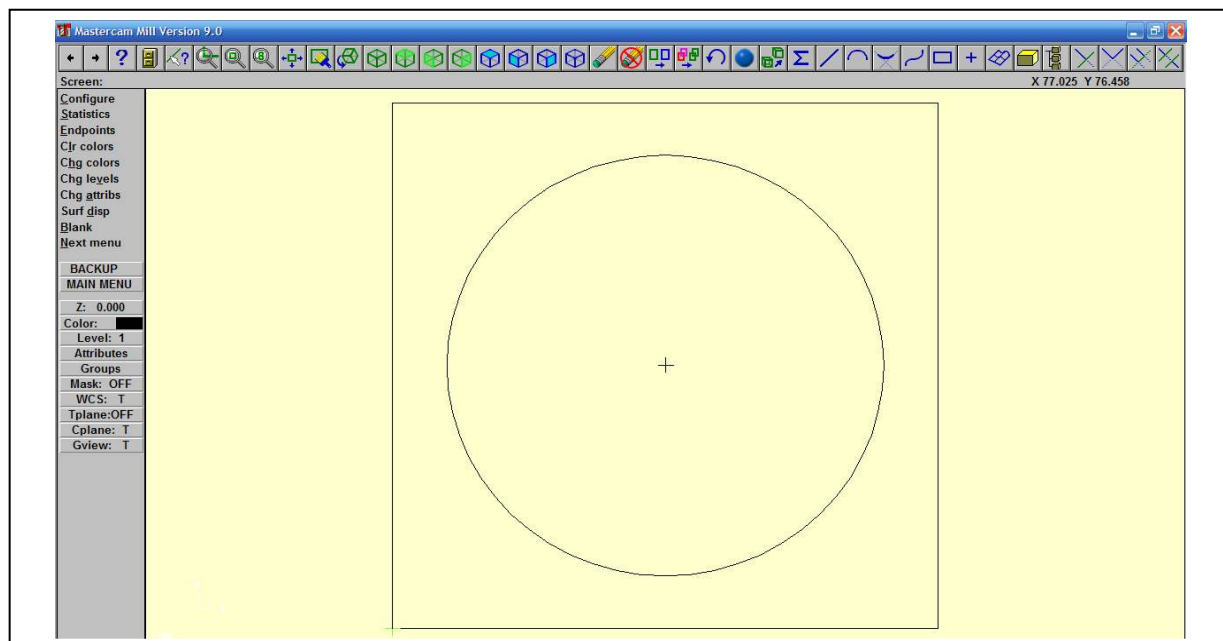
Vue du dessin de la pièce à usiner sur mastercamv9.
